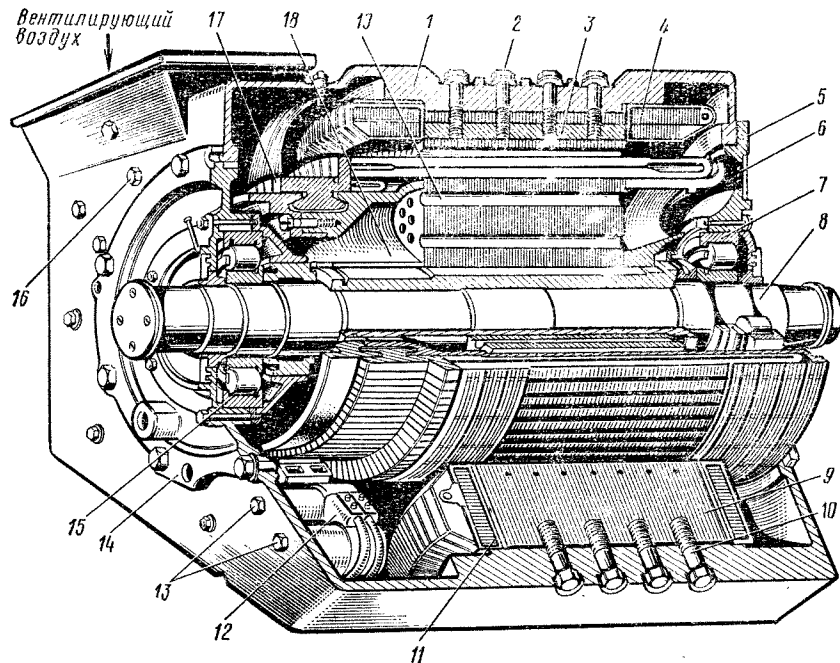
Тяговый двигатель НБ-406 в разрезе
